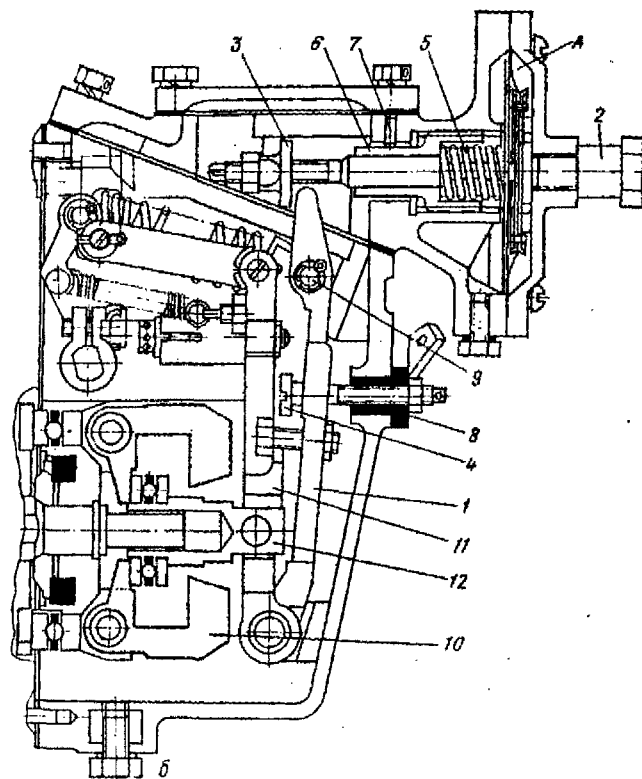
Устройство регулятора насоса 4УТНМ-Т: 1 – основной рычаг; 2 – штуцер; 3 – подвижный упор; 4 – болт номинала; 5 – пружина; 6 – втулка штока; 7 – штифт; 8 – втулка; 9 – контактная шайба; 10 – грузы; 11 – промежуточный рычаг; 12 – упорная пята; А – пневмокамера
